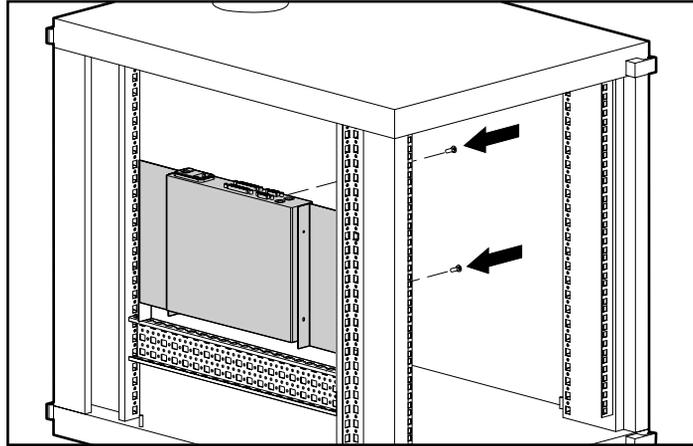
Fissaggio dell'installazione laterale a 2 porte
